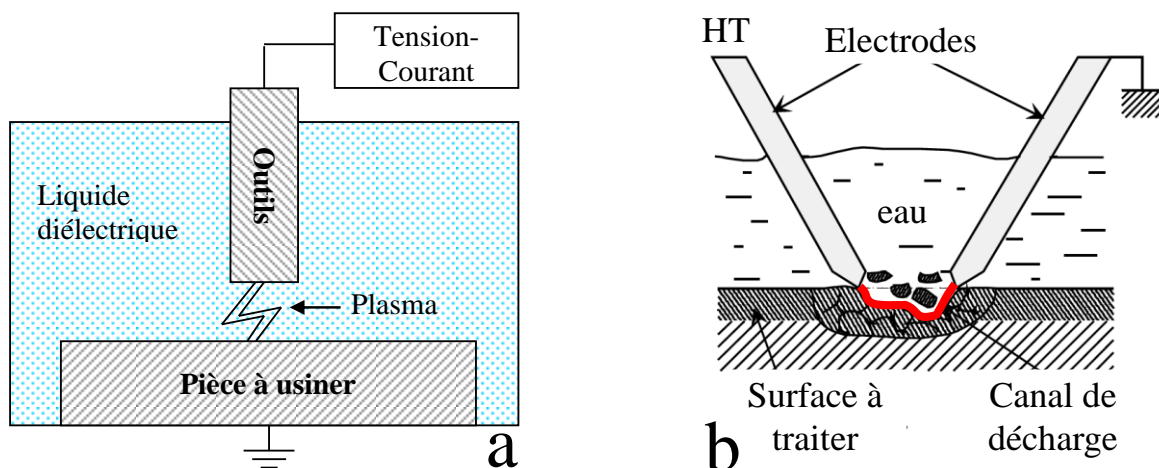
Géométries d'une machine EDM classique a) pour usiner des pièces et b) pour éroder des roches [Tou2005].
